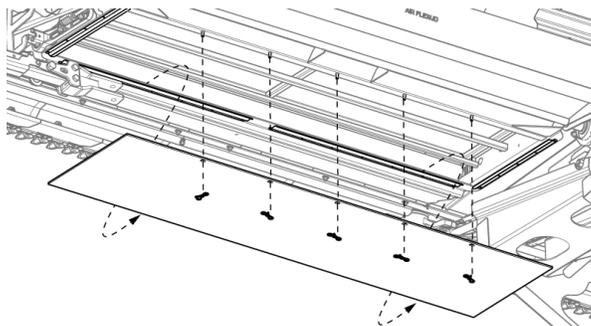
Rimozione del pannello di pulizia del draper centrale
